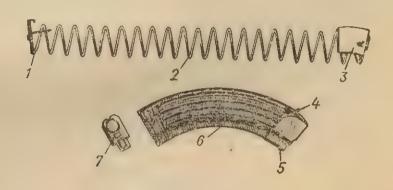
Магазин: 1 — стопорная планка: 2 — пружина: 3 — подаватель: 4 — опорный выступ; 5 — зацеп; 6 — корпус; 7 — крышка
